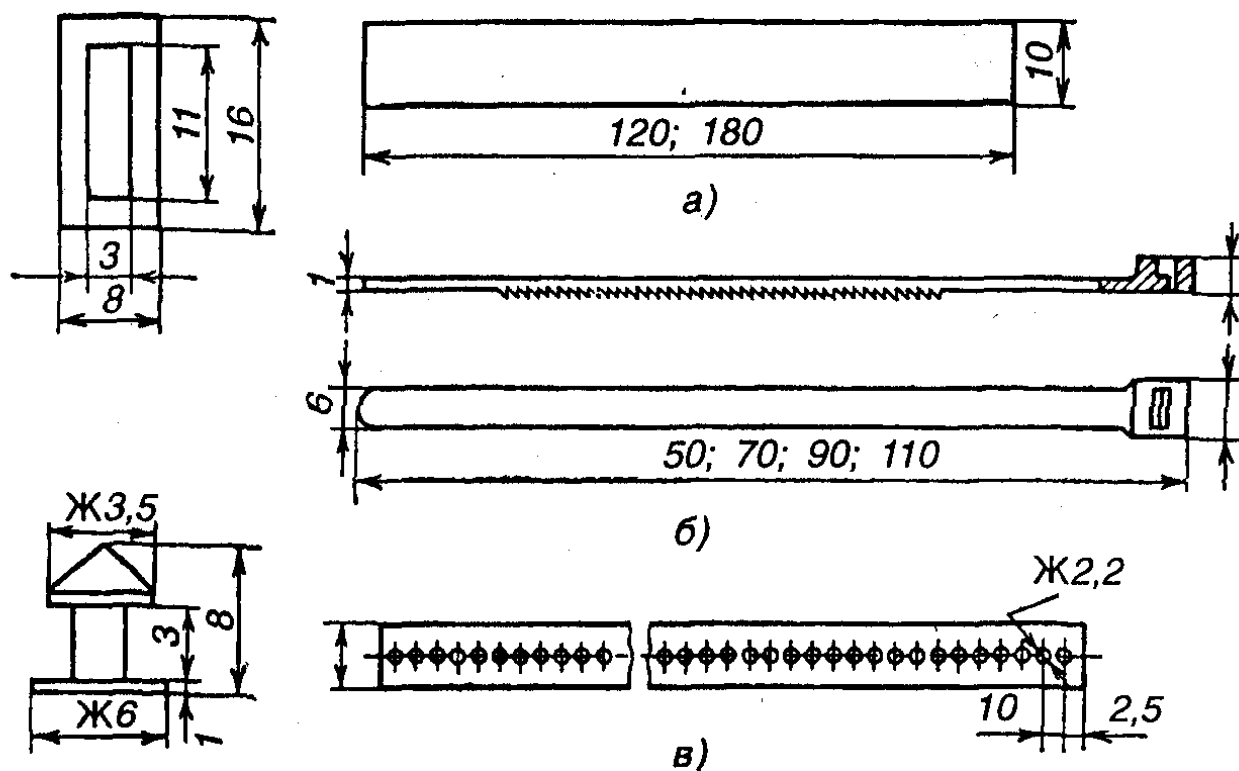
Изделия для крепления проводов, труб и кабелей:
